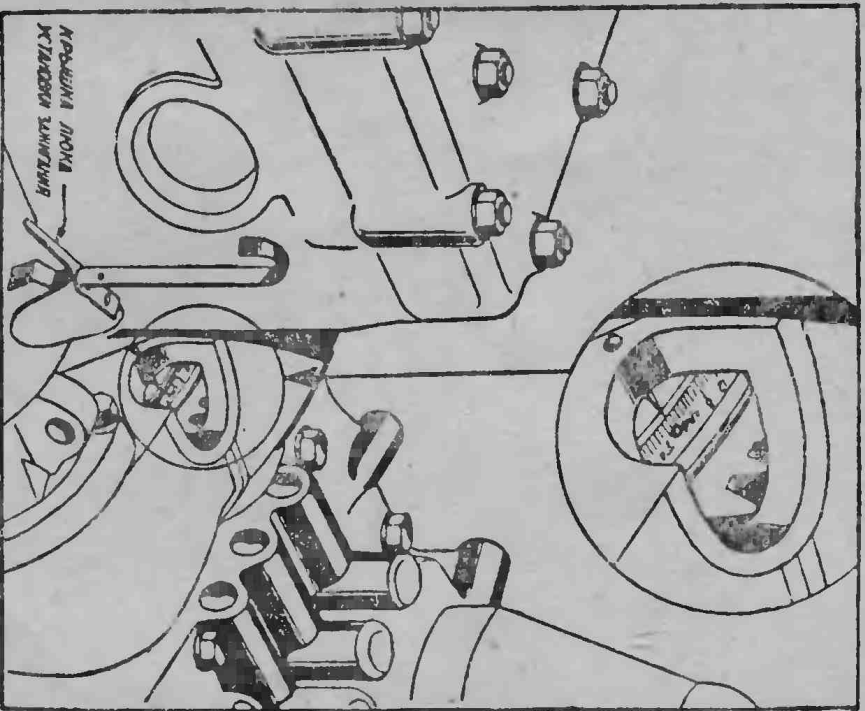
Окно для установки коленчатого вала в положение верхней мертвой точки в первом и шестом цилиндрах.
